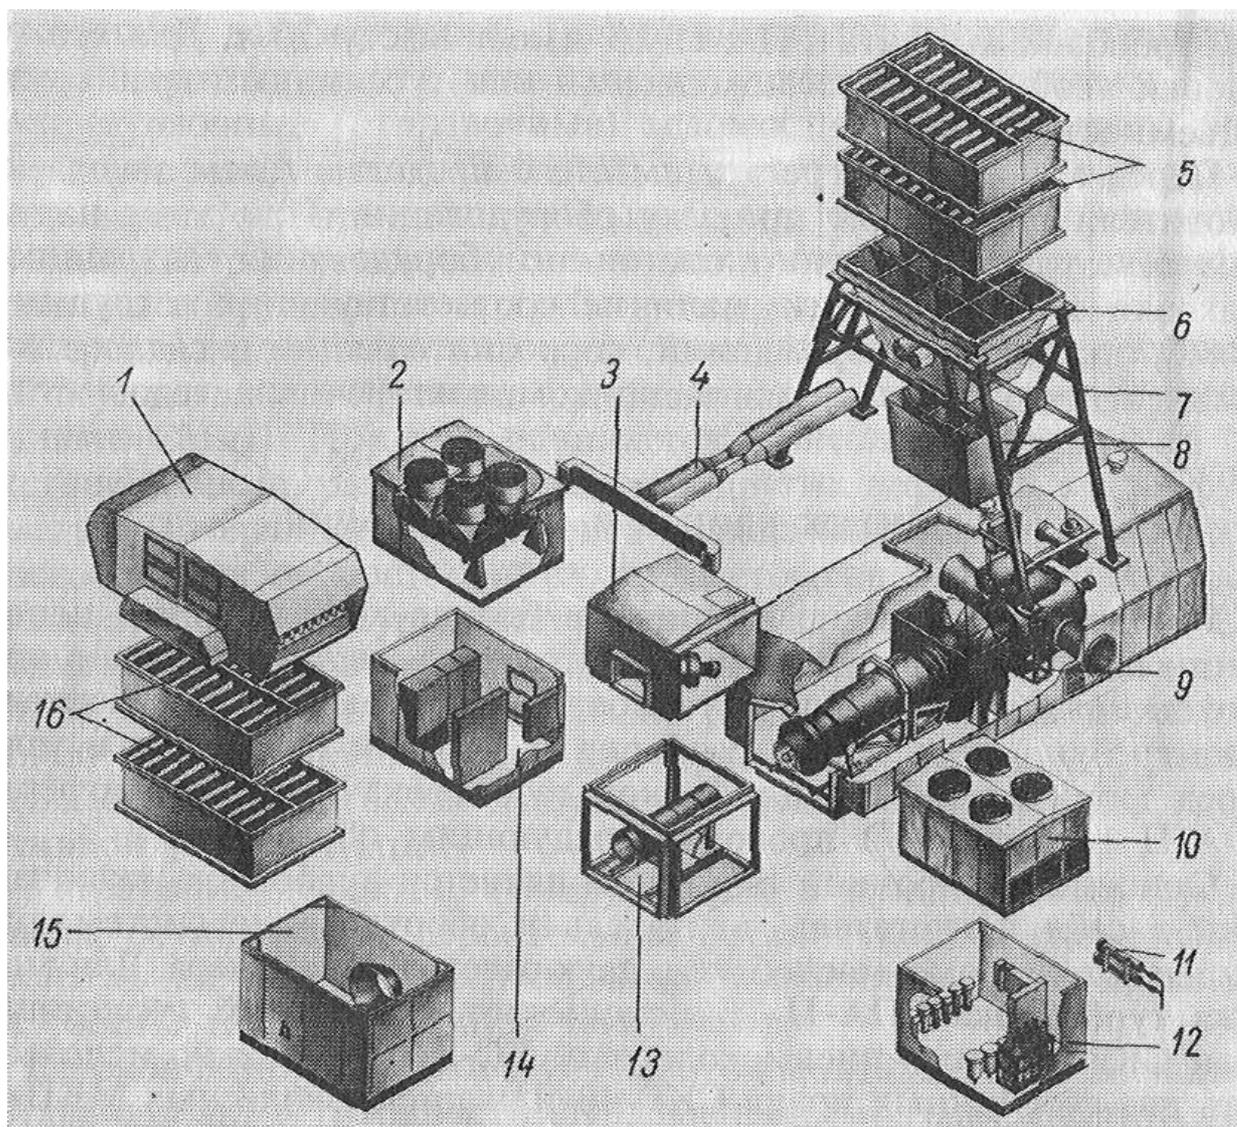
Блоки агрегата типа ГПА-Ц-16
